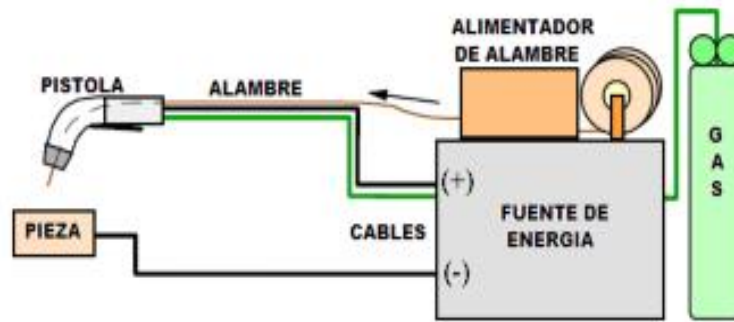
Esquema del Circuito de soldadura FCAW
